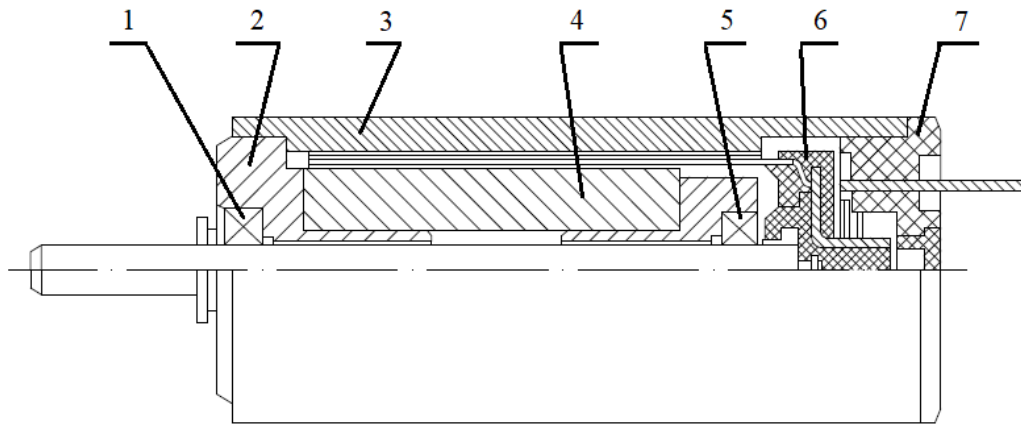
Загальний вигляд електродвигуна: 1-підшипник, 2-щит підшипниковий, 3-корпус, 4-магніт, 5-підшипник, 6-якір з колектором, 7- щіткотримач із щітками
